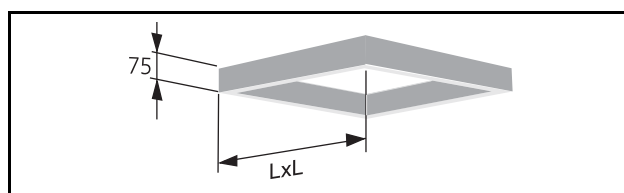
HAWK Ceiling med ALS. Lav konstruktionshøjde.
